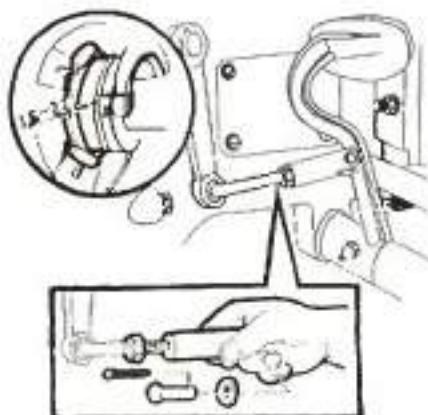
Регулировка свободного зазора муфты сцепления и свободного хода педали
